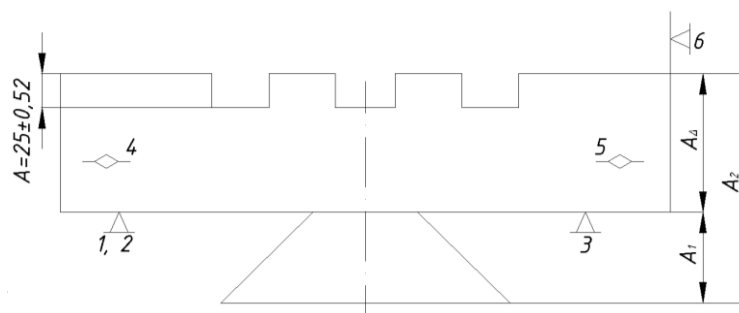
Схема базування при обробленні Т-подібних пазів
